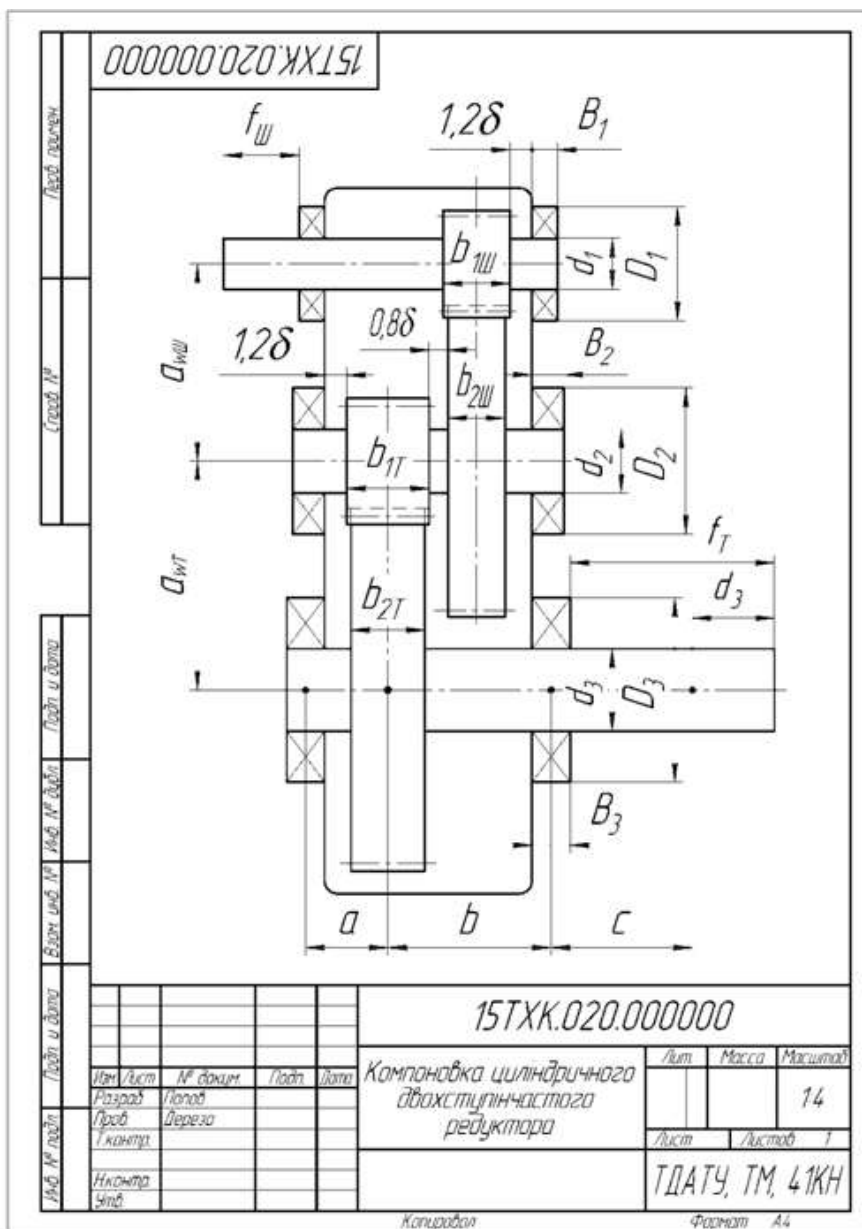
Приклад виконання ескізної компоновки редуктора
